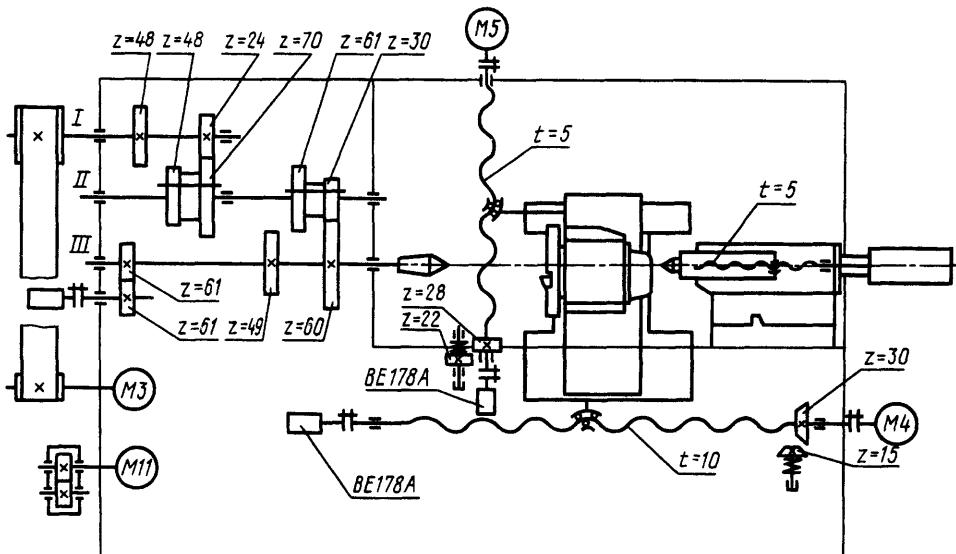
Кинематическая схема станка 16А20Ф3
